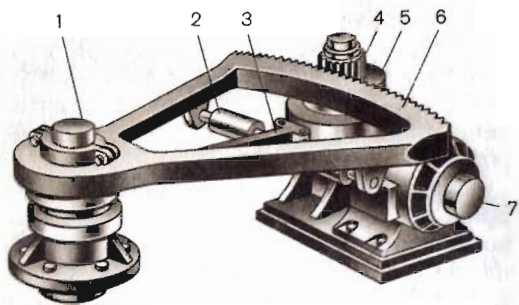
Рулевой привод с червячно-планетарным редуктором
